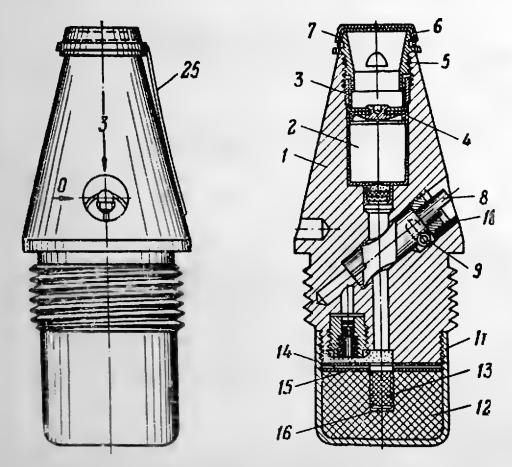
Взрыватель ГВМЗ (общий вид и разрез):
